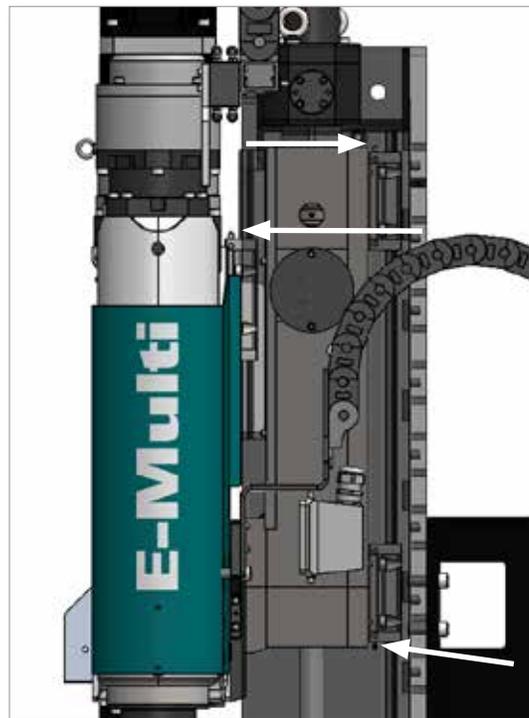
Seitenansicht (senkrecht) des ER3 mit den Schmierpunkten der Linearführungen (3)
